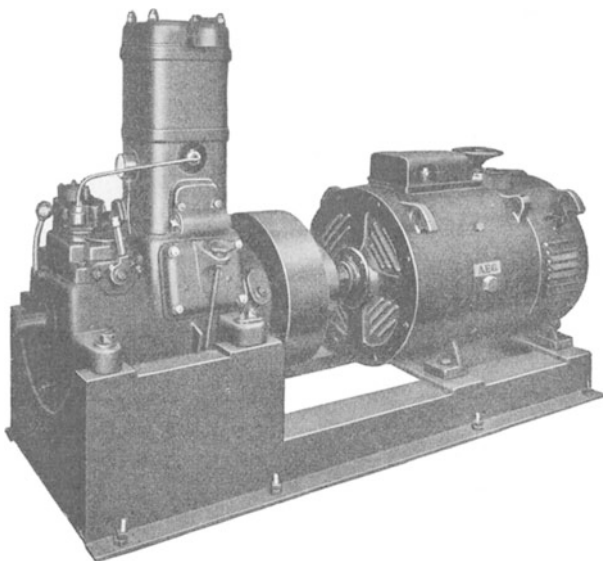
Mit Dieselmotor gekuppelte Schweißmaschine.
